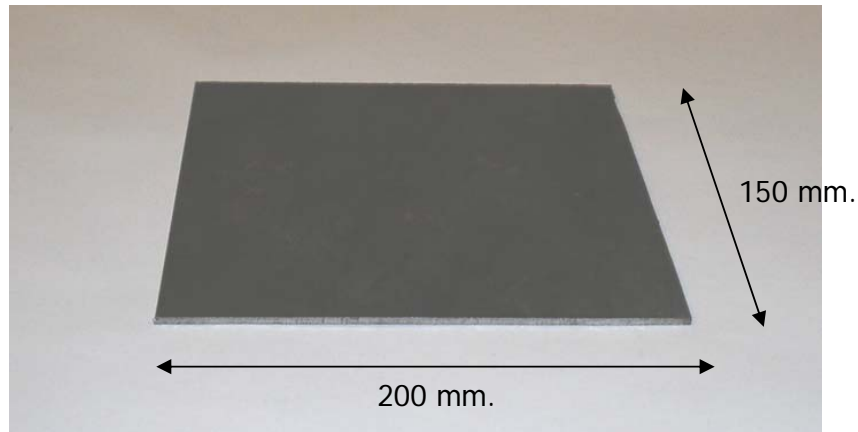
Planchas de acero ASTM A36 para la fabricación de cupones
